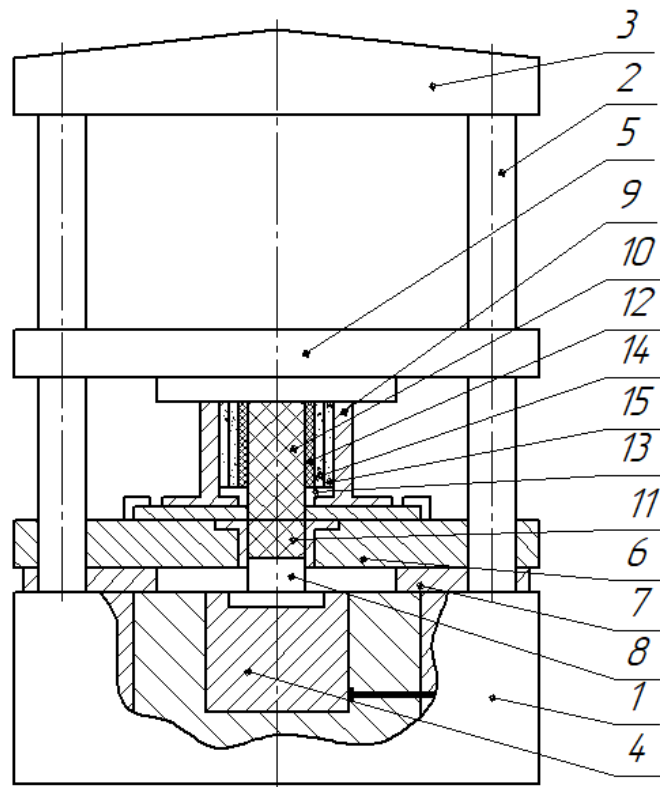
Принципиальная схема установки для изостатического прессования изделий из порошковых материалов: 1 – основание установки; 2 – направляющие колоны; 3 – верхняя неподвижная плита; 4 – плунжер гидроцилиндра; 5 – подвижная траверса; 6 – нижняя неподвижная плита; 7 – промежуточная опора; 8 – пуансон; 9 – составной контейнер; 10 – эластичный стержень; 11- эластичная вставка; 12- сменная эластичная втулка; 13- опорная втулка; 14 – камера засыпки для порошка внутреннего слоя; 15 – камера засыпки для порошка наружного слоя.
